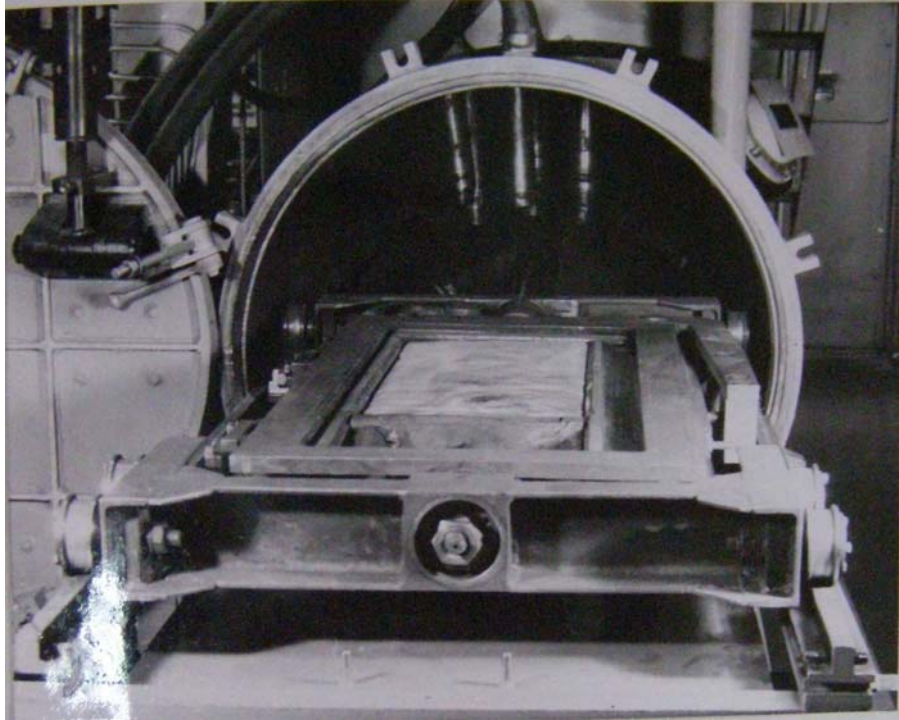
Внутрішній вид камери і розміщення зливка на візку
